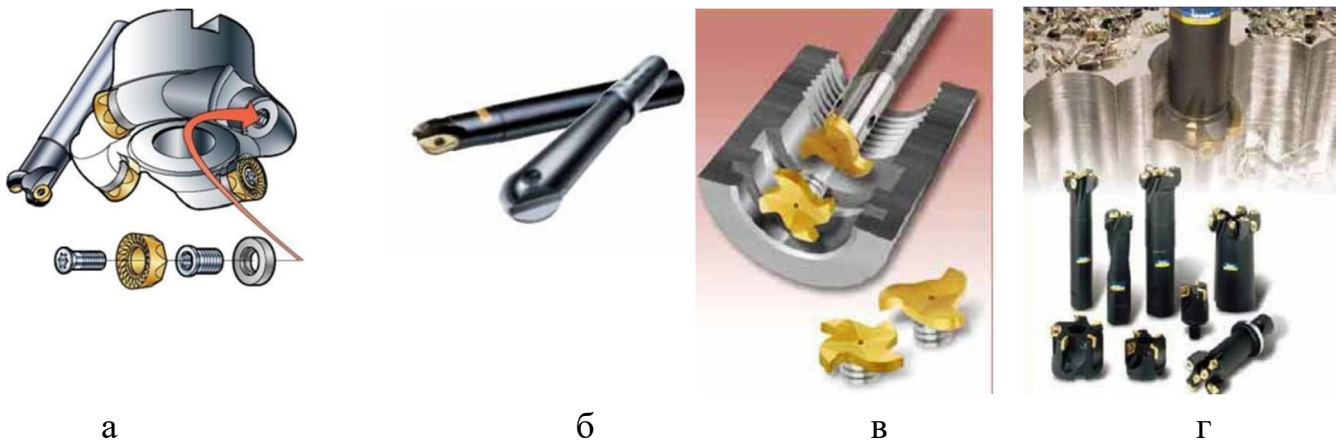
Фрези CoroMill 200 (а); CoroMill R216 і CoroMill R216F (б);
